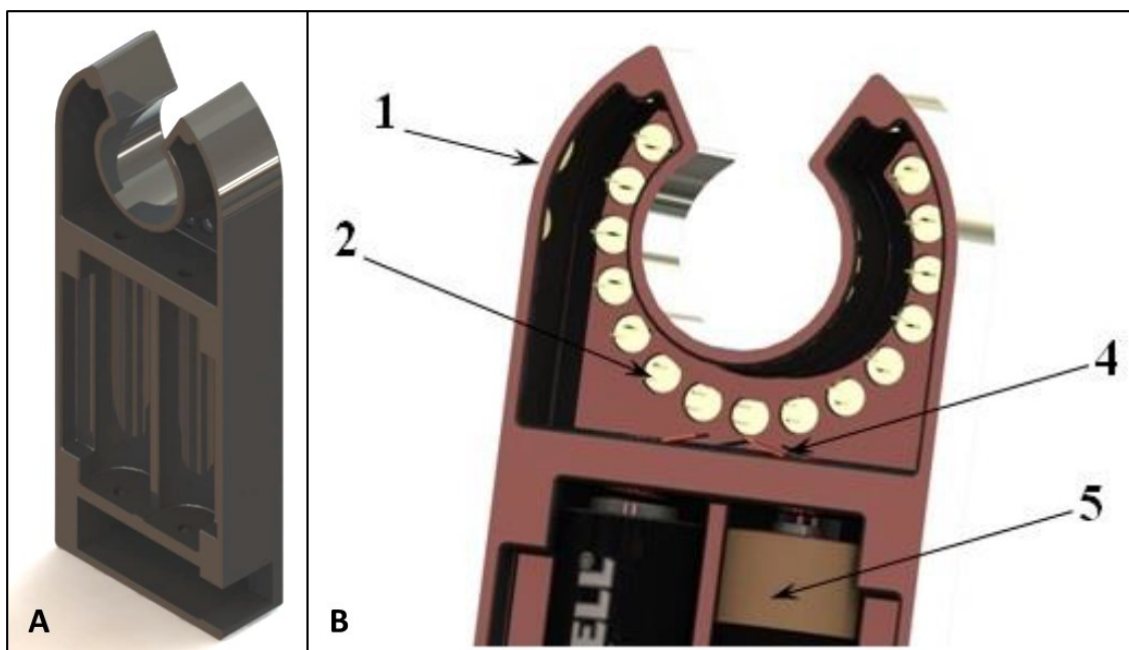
Base do dispositivo transiluminador vascular: A) componente base; B) vista frontal da componente base (1); lâmpadas de LED (2); contatos (4); pilhas AA (5).
